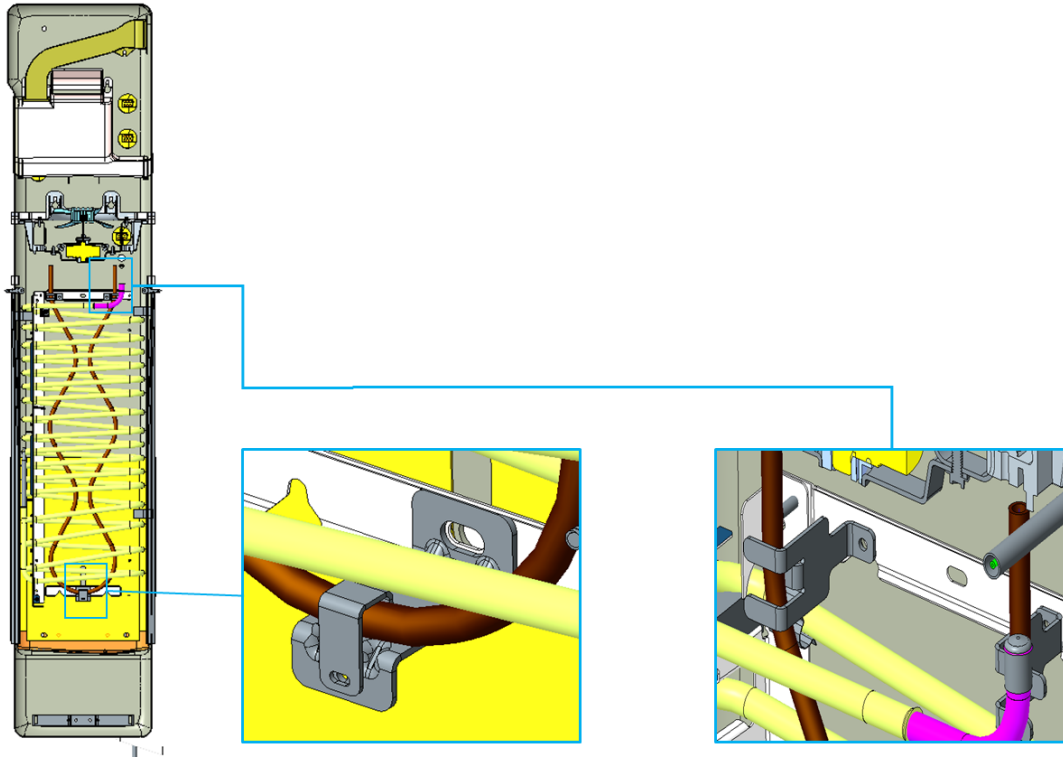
Imagen del montaje de la propuesta 2 en CAD
